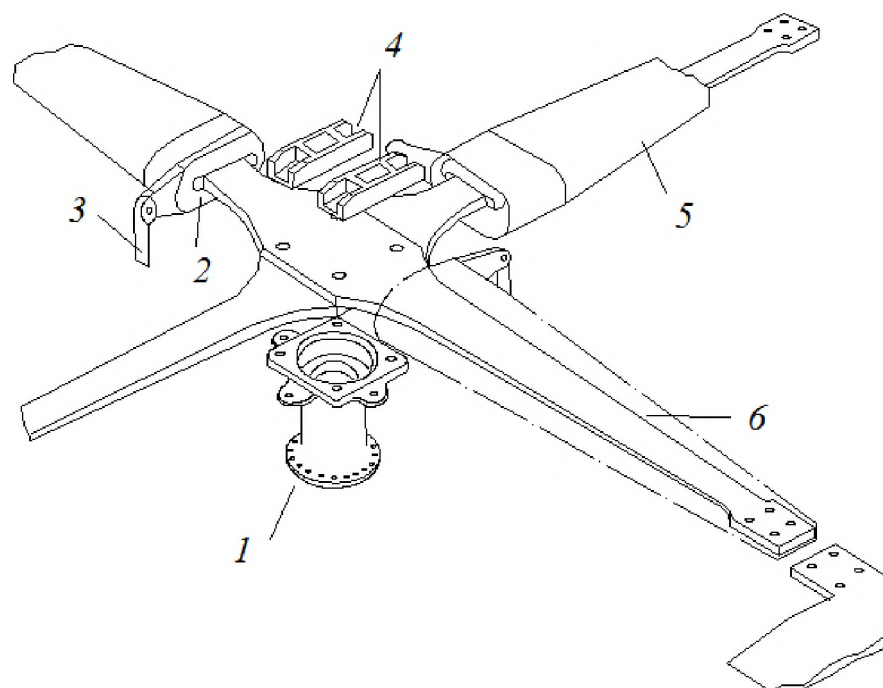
Схема втулки НВ с упругими торсионами балочного типа:
